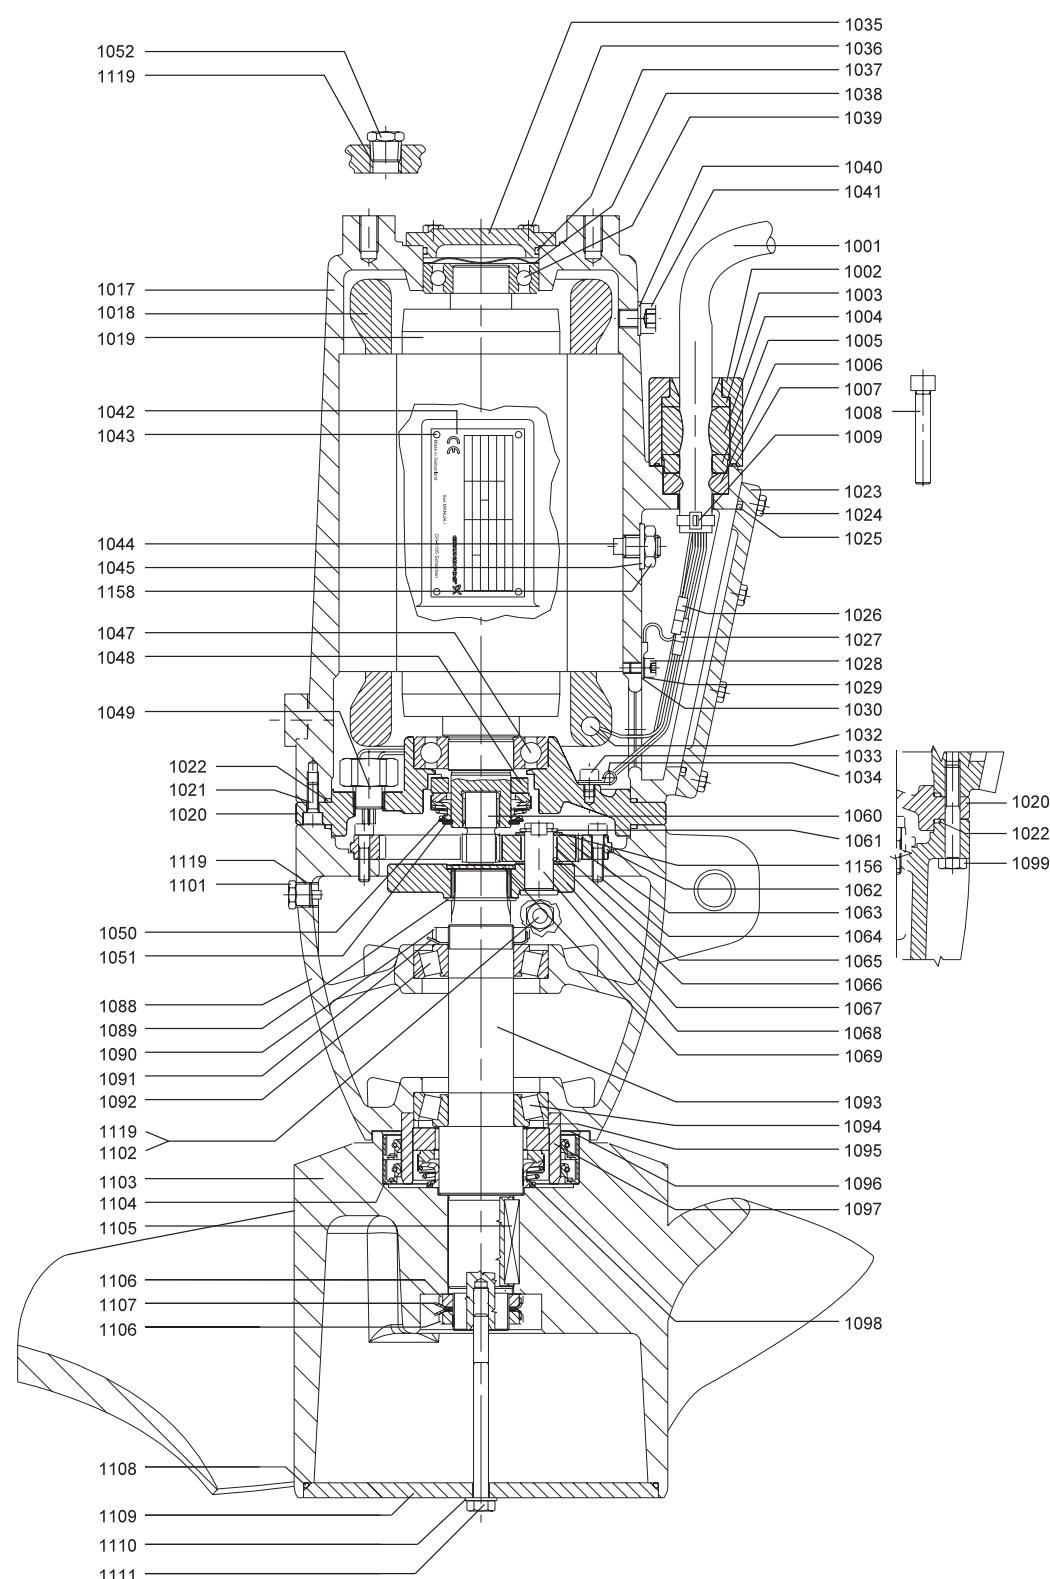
Чертёж в разрезе, SRP.35.50.xxx, SRP.50.30.xxx
